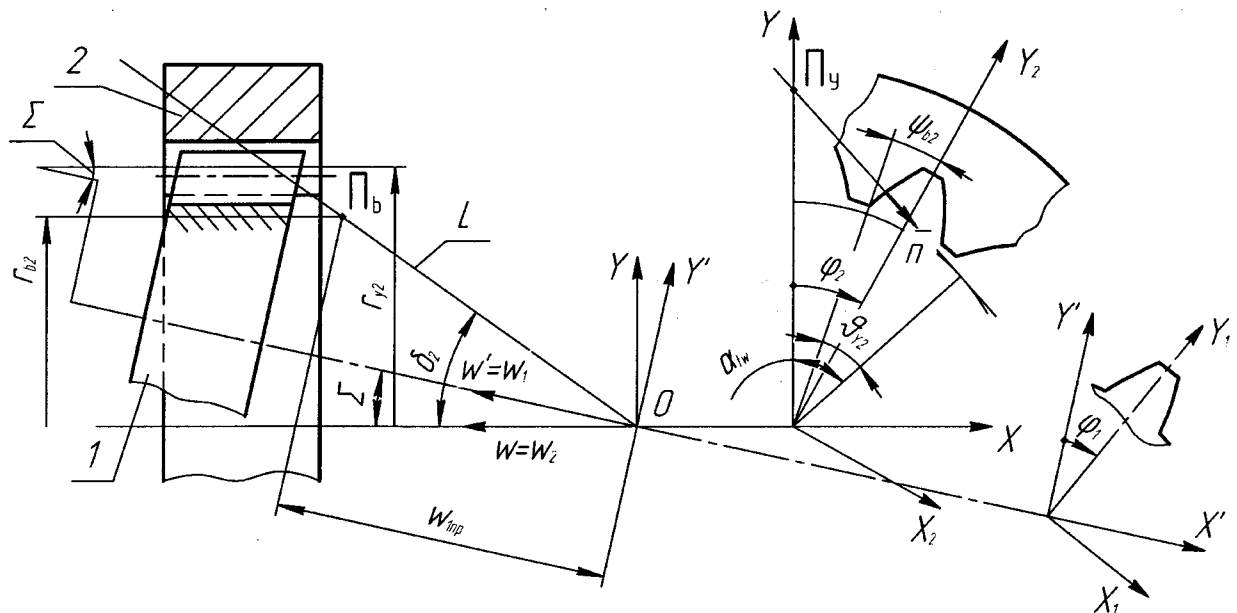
Станочное зацепление производящего колеса (2) и конической шестерни (1)
